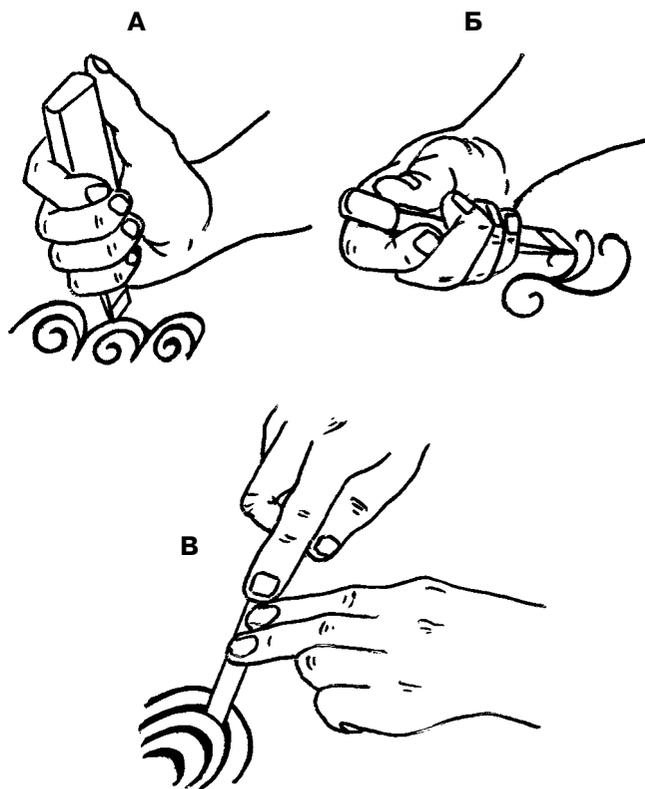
Техника плоско-рельефной резьбы с закругленными контурами:
